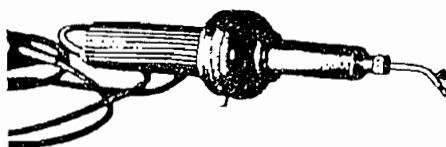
Soplete de soldar por gas calentado eléctricamente.
